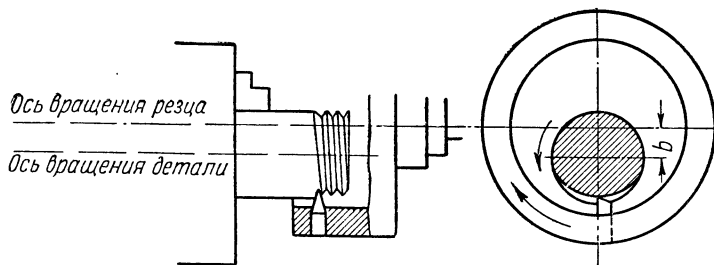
Приспособление для нарезания резьбы вращающимися резцами.
